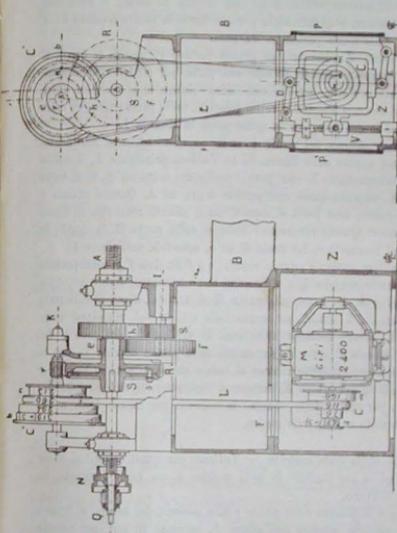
Schema di disposizione del tornio Dubosc con motore elettrico.
